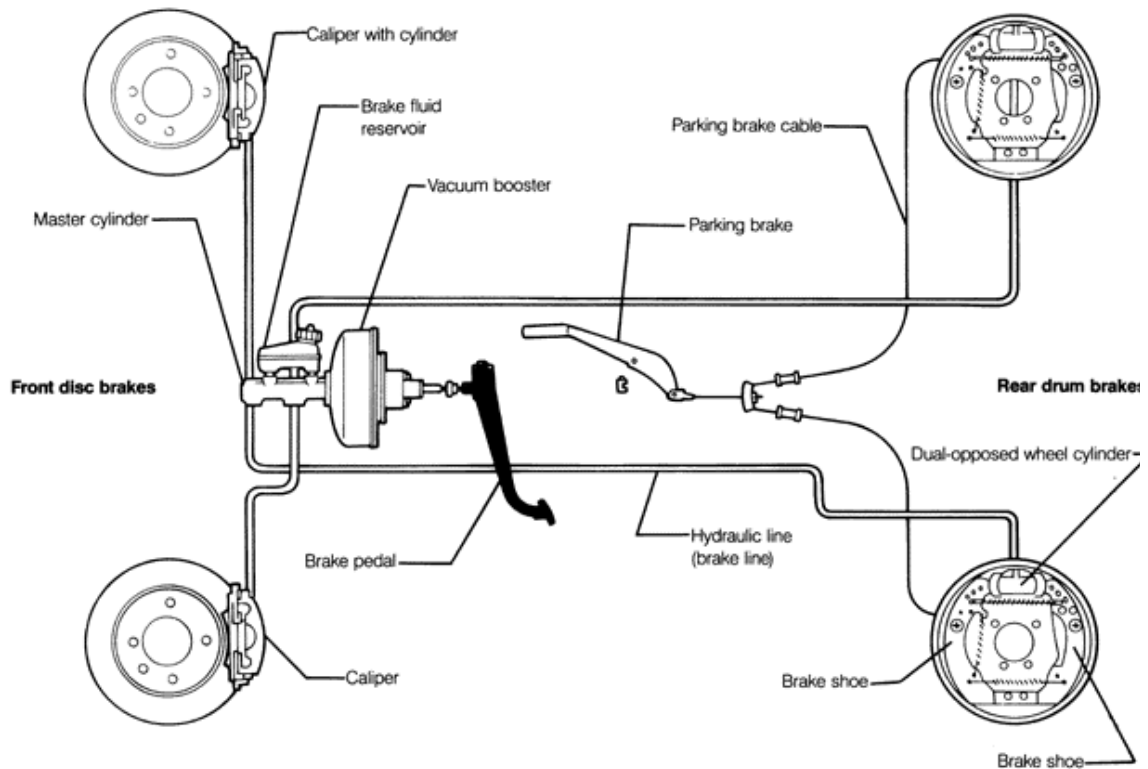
Sistema de freios automotivo comum (www.carparts.com)
